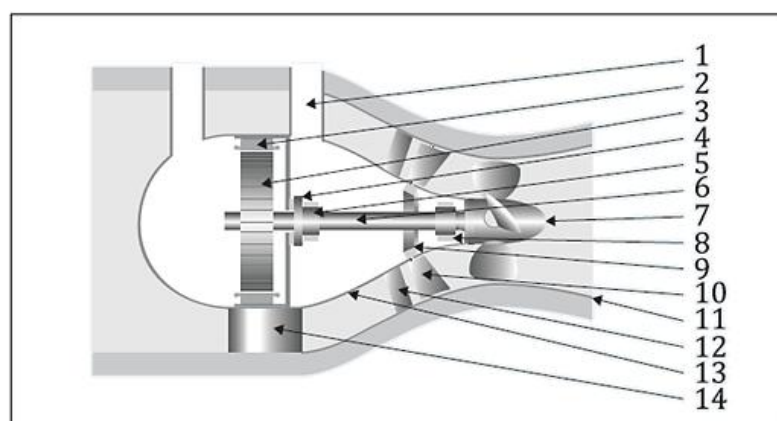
Компоненти капсульного гідроагрегату: 1 – доступ до вала; 2 – статор; 3 – ротор; 4 – упорний підшипник; 5 – напрямний підшипник генератора; 6 – вал; 7 – турбіна; 8 – напрямний підшипник турбіни; 9 – опора; 10 – напрямний апарат; 11 – тягова труба; 12 – флюгер; 13 – корпус; 14 – нижня опора.
